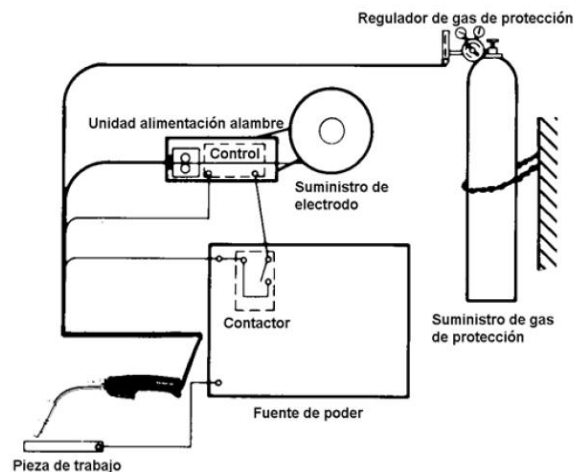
Sistema de Soldadura GMAW.
